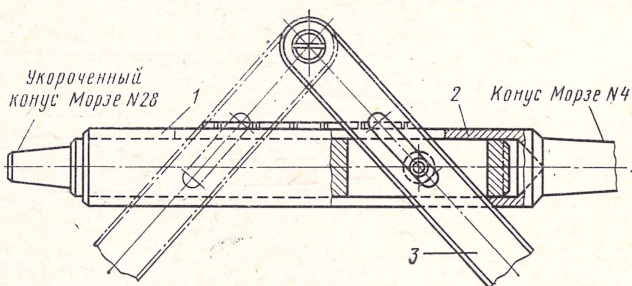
Приспособление для безопасного сверления глубоких отверстий
